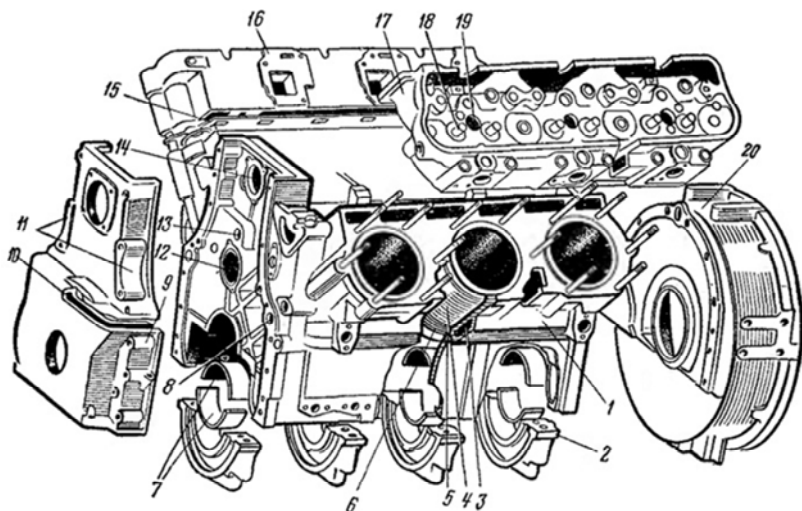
Блок и головки цилиндров двигателя ЯМЗ-236:
